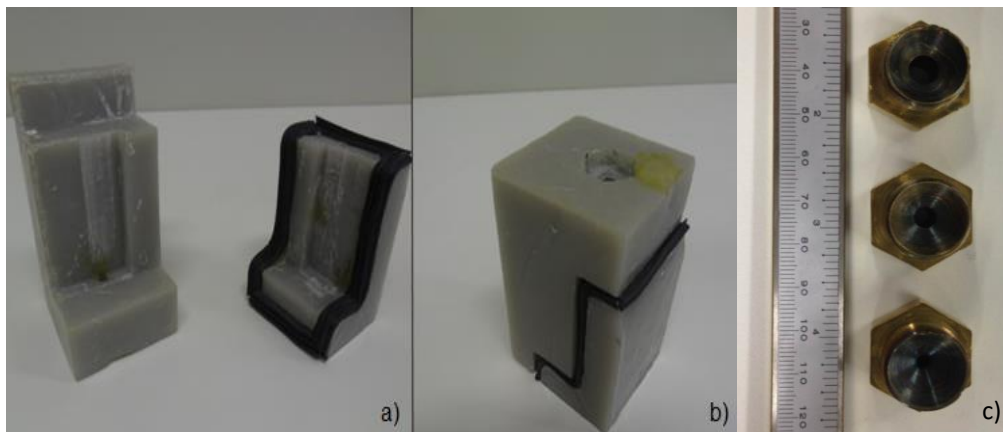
Molde em epóxi para a injeção: a) molde aberto e b) molde fechado e c) bicos injetores
